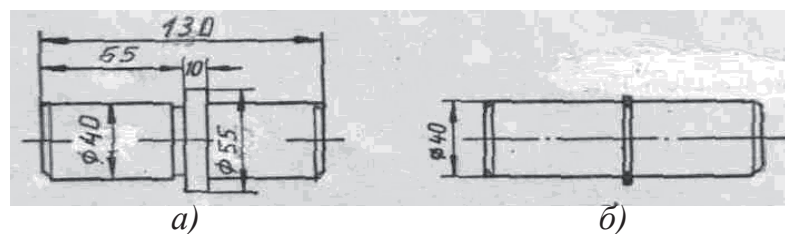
Две возможные конструкции валика: а – ступенчатый валик; б – гладкий валик с канавкой для стопорного кольца
